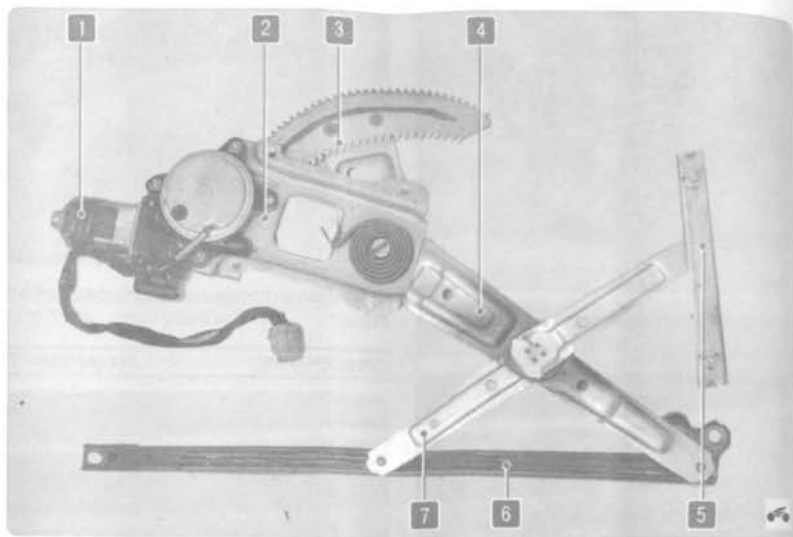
Стеклоподъемник передней двери: 1 – моторредуктор; 2 – кронштейн крепления стеклоподъемника; 3 – зубчатый сектор моторредуктора; 4 – рычаг привода обоймы стеклоподъемника; 5 – регулировочная планка стеклоподъемника; 6 – ползун обоймы стекла; 7 – рычаг ползуна
